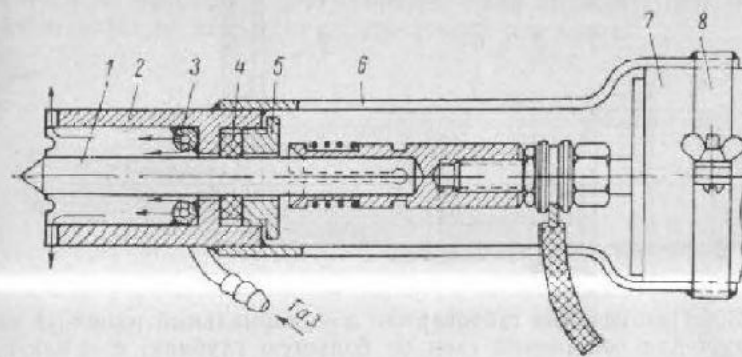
Насадка для подачи защитного газа в зону сварки.
